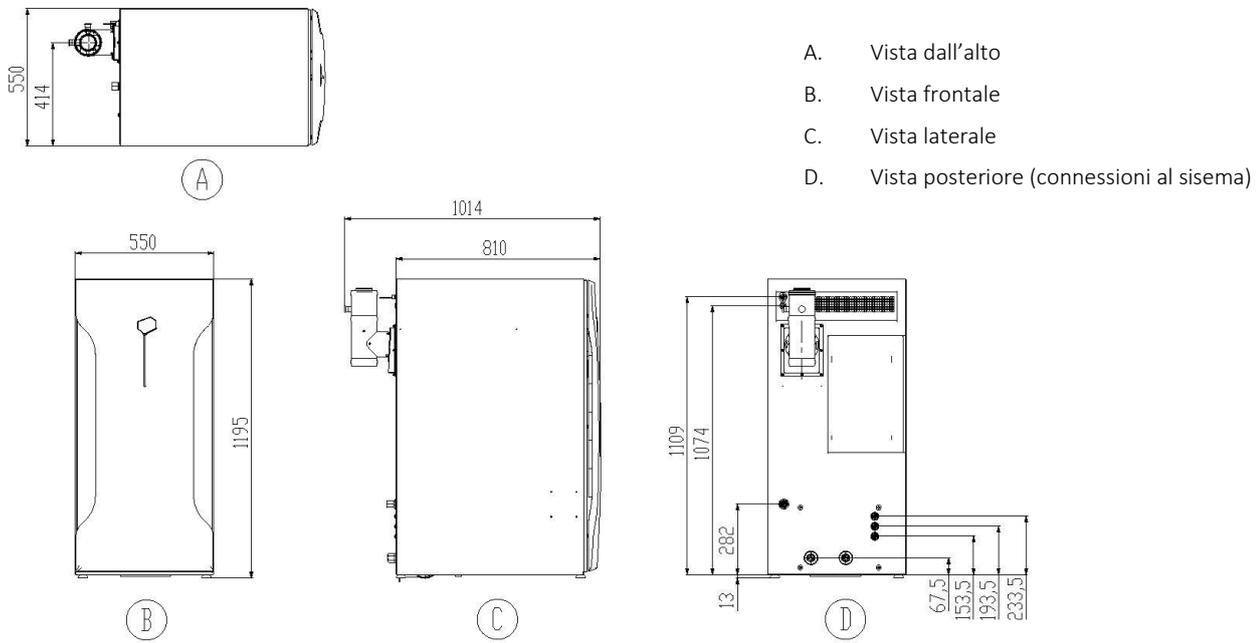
Dimensioni del BLUEGEN BG-15 (mm)
